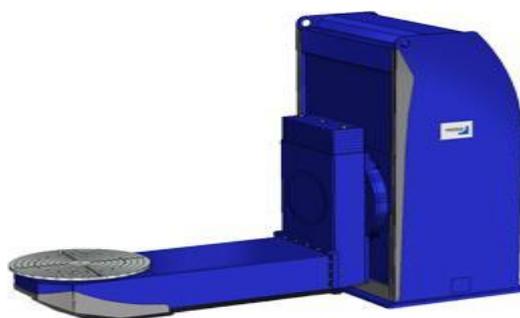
Сварочный манипулятор Skyhook SPS-750
